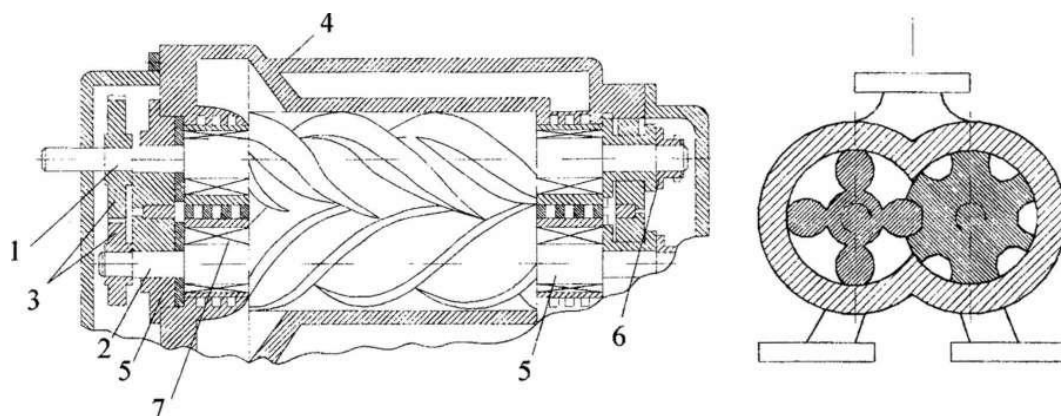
Винтовой компрессор: 1 - ведомый вал; 2 - ведущий вал; 3 - шестерни синхронизации; 4 - корпус; 5 - опорные подшипники; 6 - упорные подшипники; 7 - узел уплотнения
